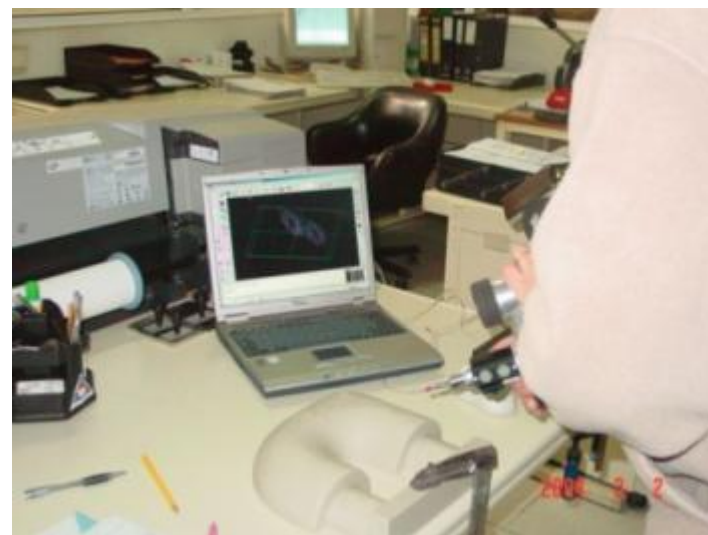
Controlo dimensional com braço tridimensional de medição FARO®
